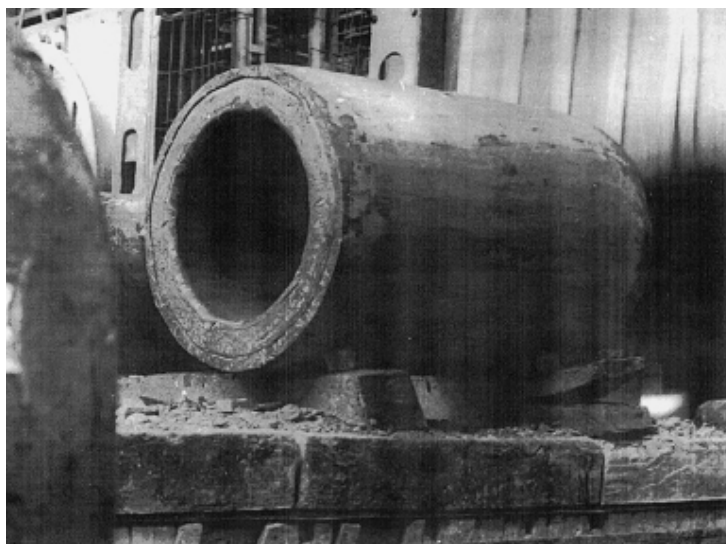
Заготовка (поковка) под восстанавливаемый составной валок массой 43 тонны
